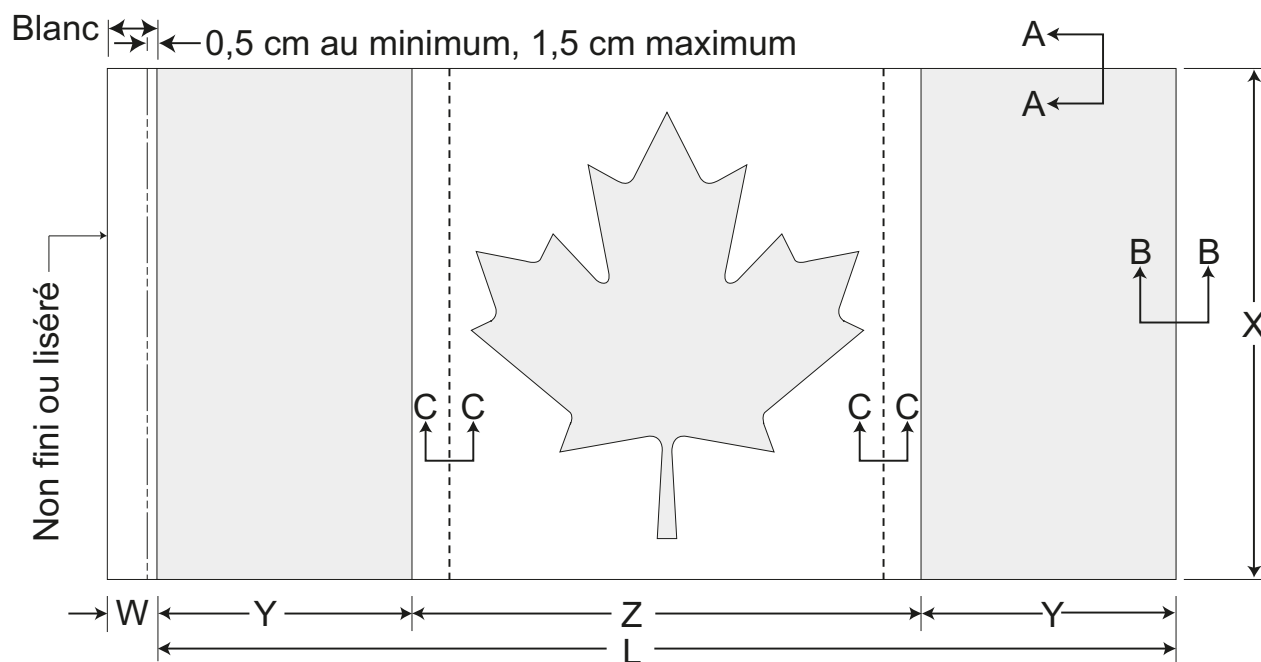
Fabrication d'un drapeau constitué de trois pièces de tissu
